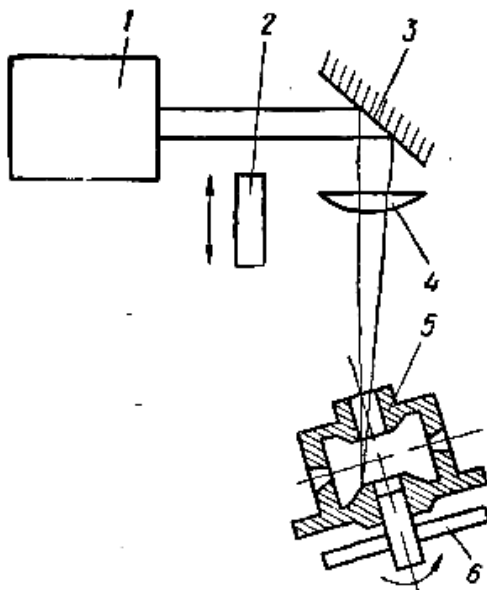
Схема лазерної установки для зміцнення циліндричних поверхонь:
